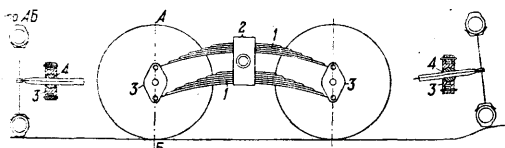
1—рессора; 2—башмак, качающийся около неподвижной поперечины; 3—хомуты крепления концов рессор; 4—шаровые вкладыши, связанные с кожухами ведущих осей.
